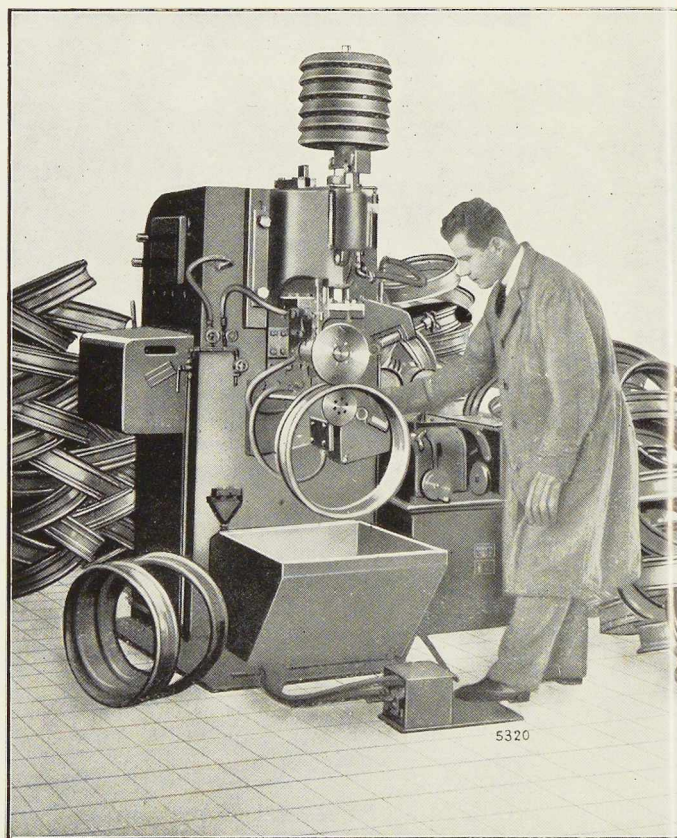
Machine à souder au galet spécialement étudiée pour la soudure des jantes d'automobiles.
